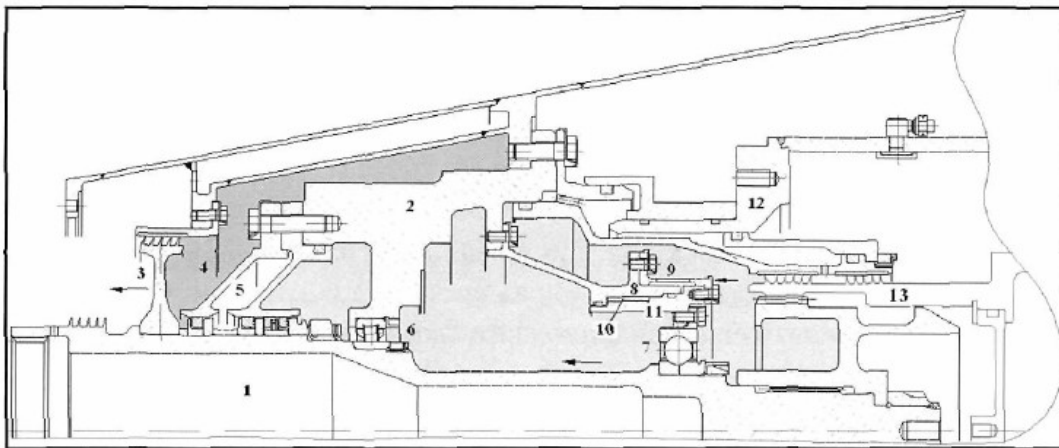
Конструкція проміжної опори із змінною жорсткістю для компресорного стенду:
